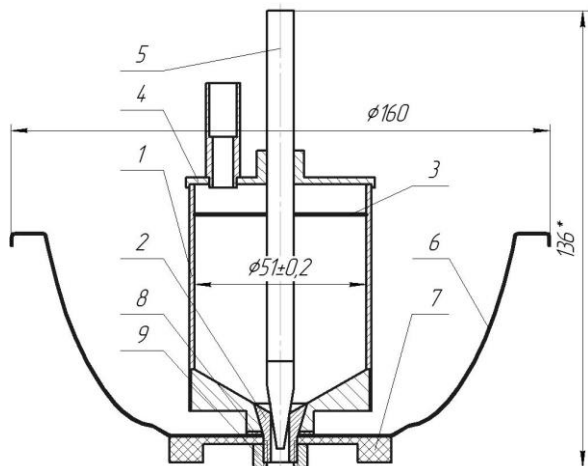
Вискозиметр ВЗ-1: 1 – Внутренний резервуар; 2 – Сопло; 3 – Риска; 4 – Крышка; 5 – Стержень; 6 – Ванна (Наружный резервуар); 7 – Опора наружной ванны; 8 – Уплотнение между резервуарами; 9 – Гайка фиксирующая.
